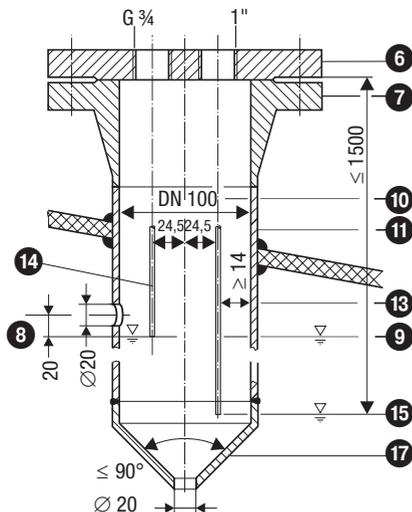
Tubo di calma di protezione (da prevedere sul posto) per installazione all'interno della caldaia previsto per montaggio di un secondo apparecchio GESTRA
